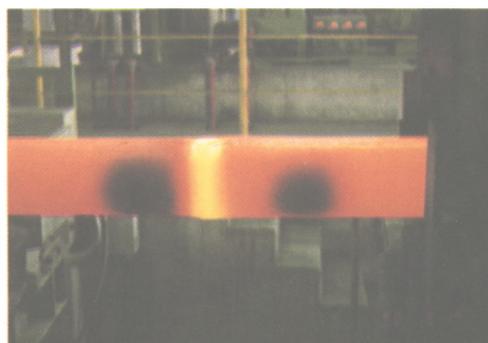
Сварка заготовок при бесконечной прокатке
